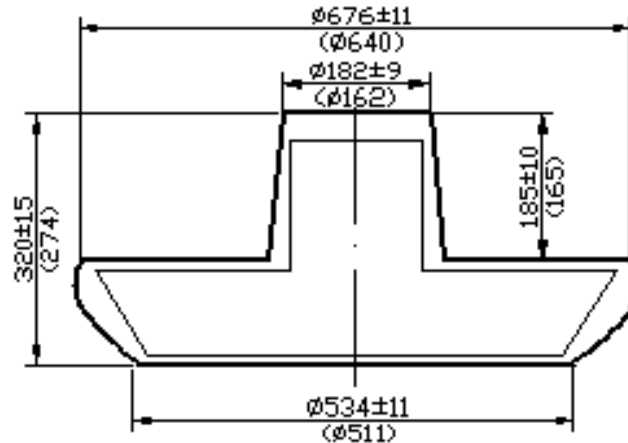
Креслення одержуваної заготовки при використанні нового способу штампування
